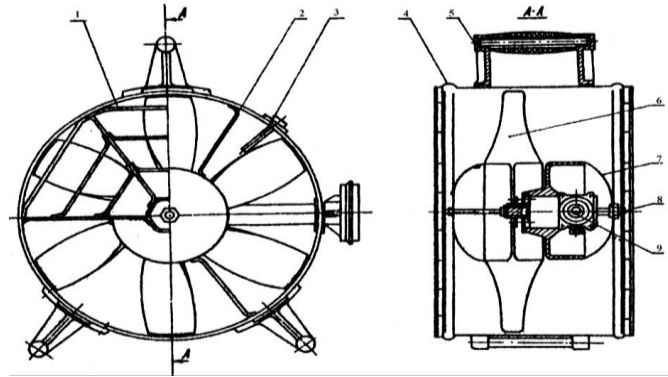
Димовсмоктувач ДП-7: 1 – захисна сітка; 2 – спиця; 3 – термометр; 4 – корпус; 5 – ручка; 6 – робоче колесо; 7 – обтікач; 8 – маслянка; 9 – редуктор
